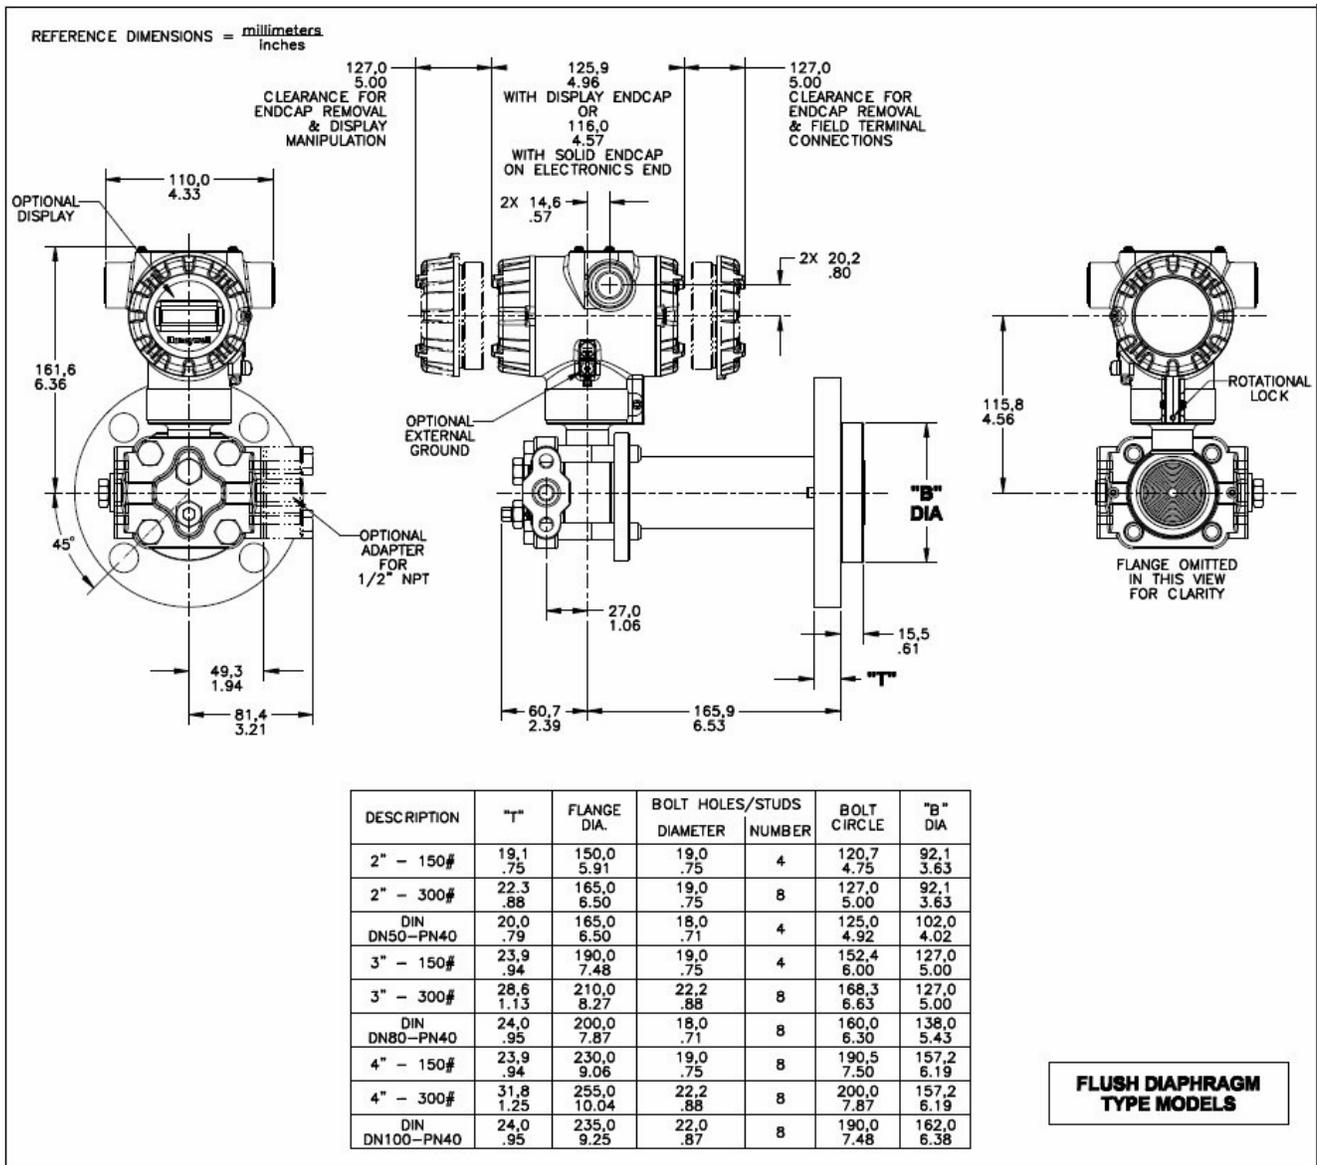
Dimensiunile de Montaj pentru conectare directa prin diafragme la modelele STF828 si STF832.
